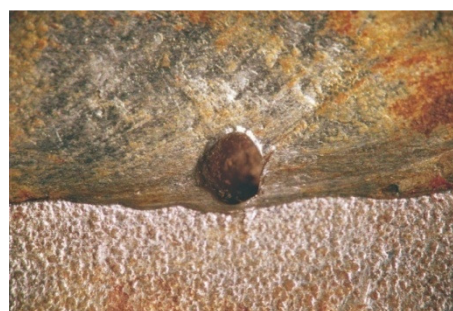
Picadura en zona del cordón de soldadura de plancha del piso (16X).
